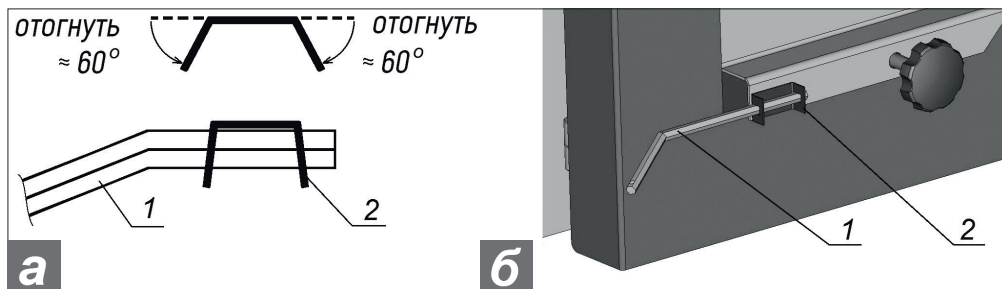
Схема гибки пластинки (а) и установка (б) шестигранного стержня:
